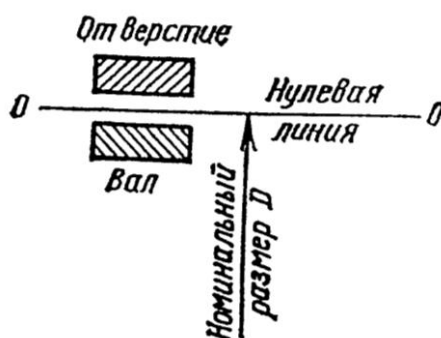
Поля допусков отверстия и вала при посадке с зазором
